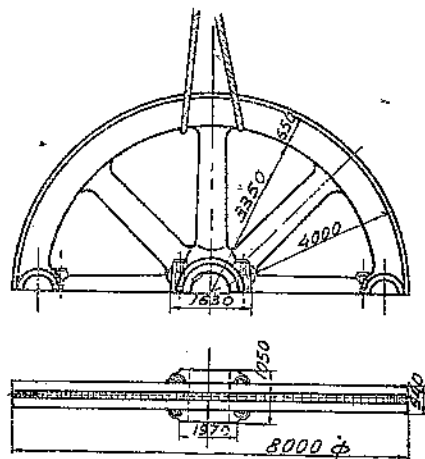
Вид маховика колеса газовой машины ДТ-16 в сборе.
